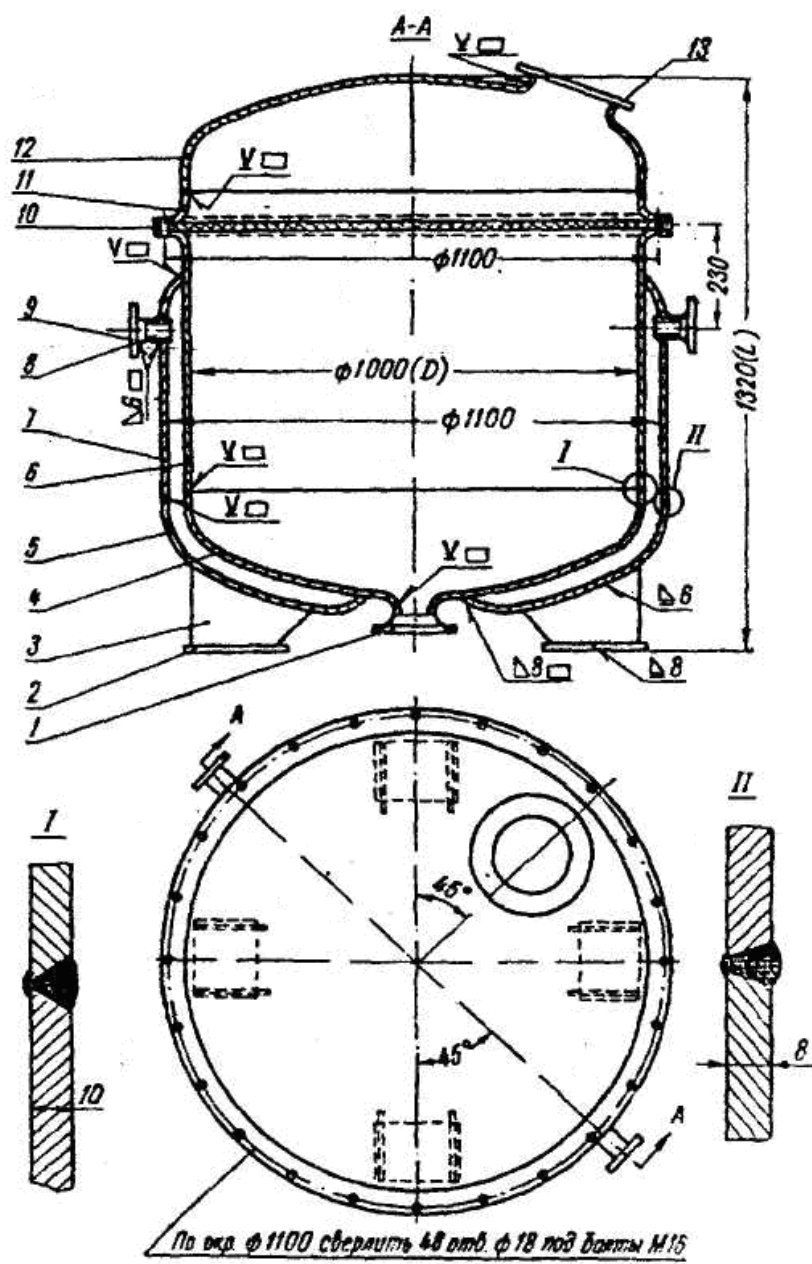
Эскиз корпуса варочного аппарата для задания № 4
